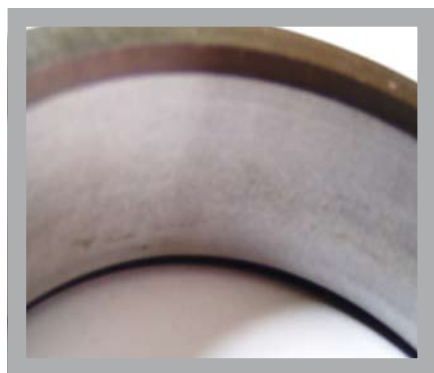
Матовая поверхность внутреннего кольца подшипника при неподвижной посадке на вал
